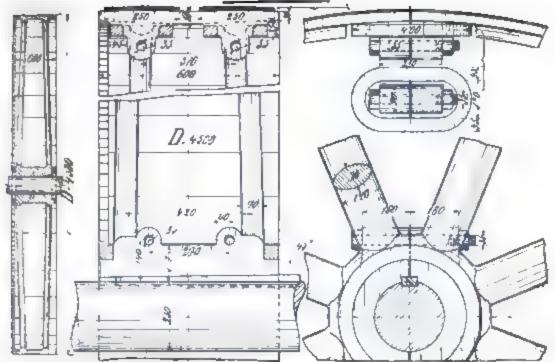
708. Schwungrad, 4500 mm Durchm, für zichten, geböreud zu einer Kompoundmaschine d—850, D—325, H—700, n=40, z. Antriebzweier Dynamos.
